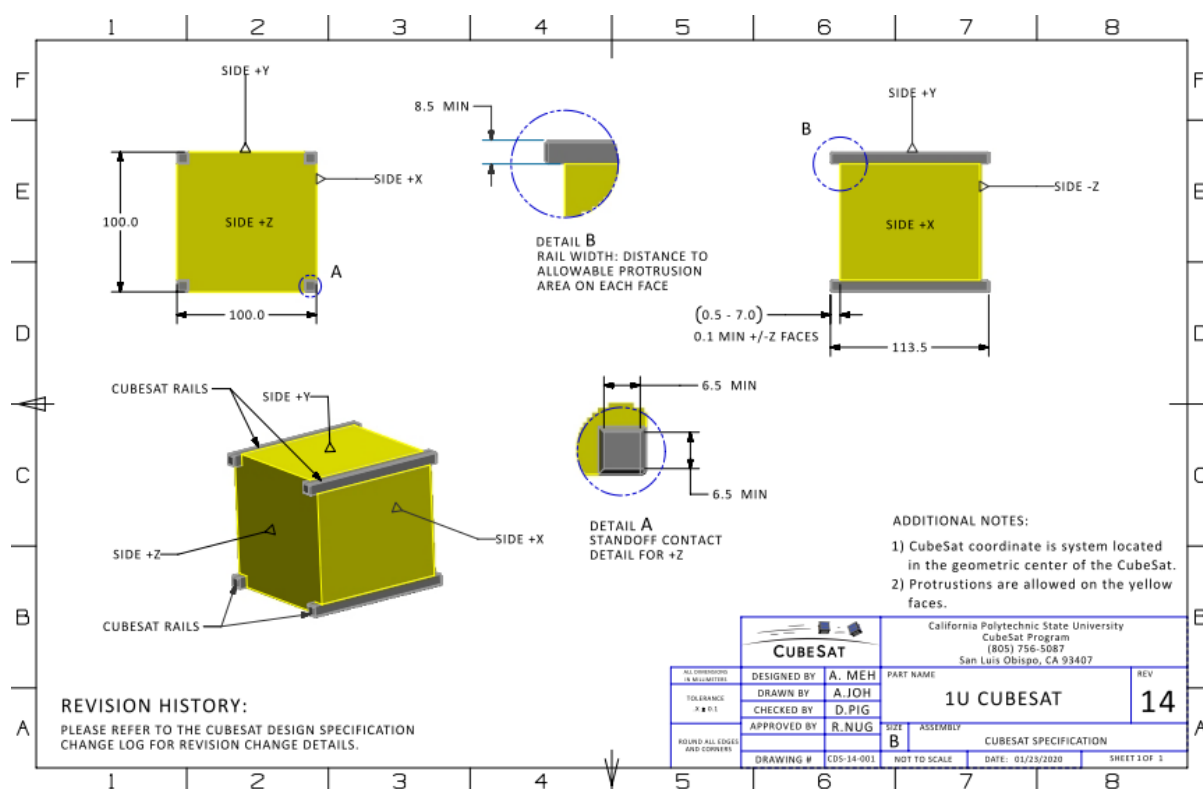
Чертеж спутника форм-фактора Cubesat 1u
